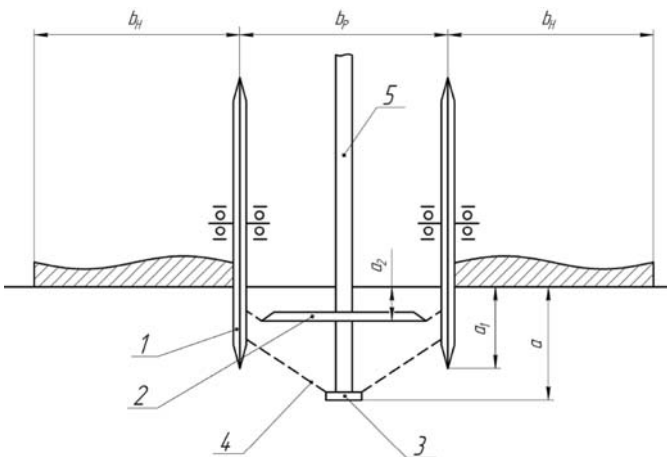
Схема ґрядля агрегата смугового обробки ґрунту:
